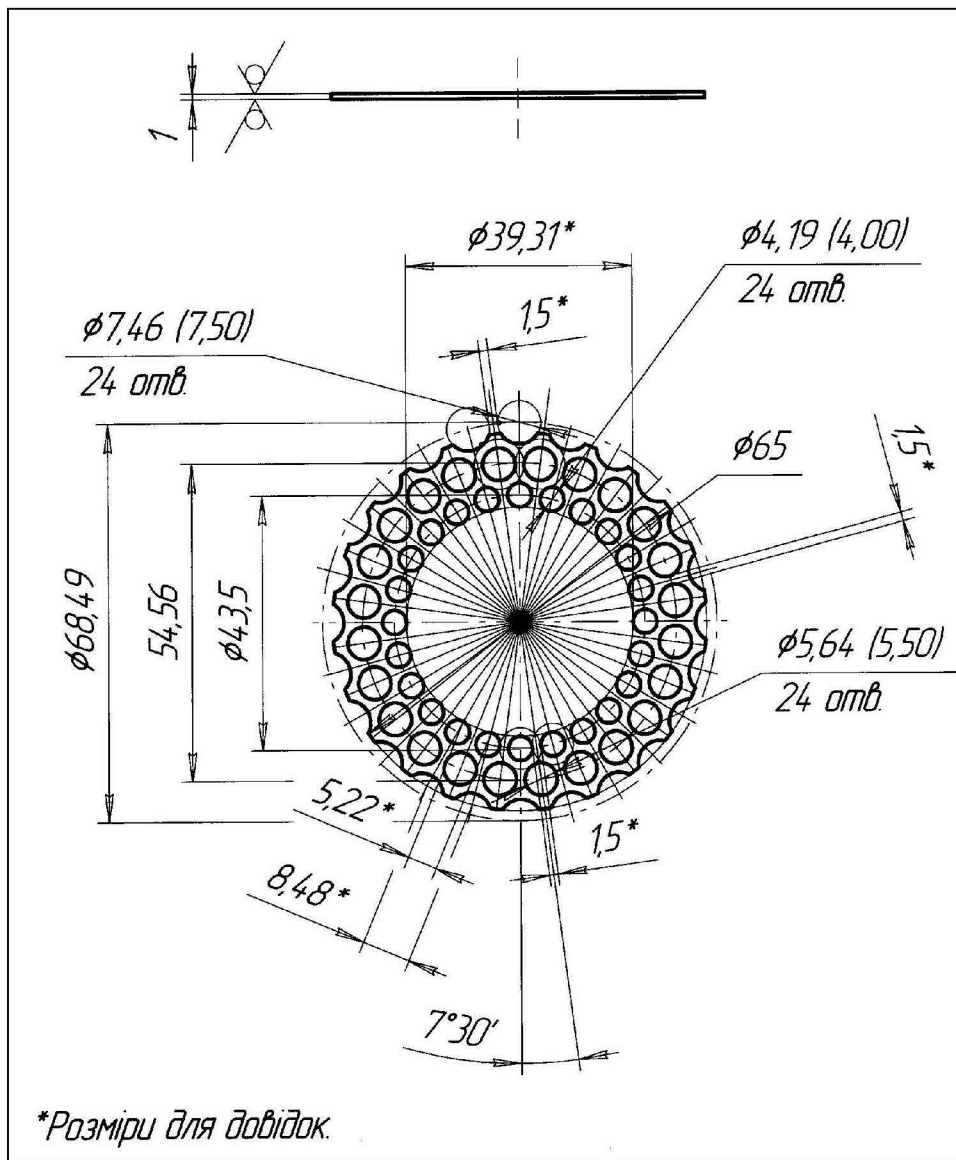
Креслення розрахункової вихідної заготовки для витягування за новим способом, що пропонується
